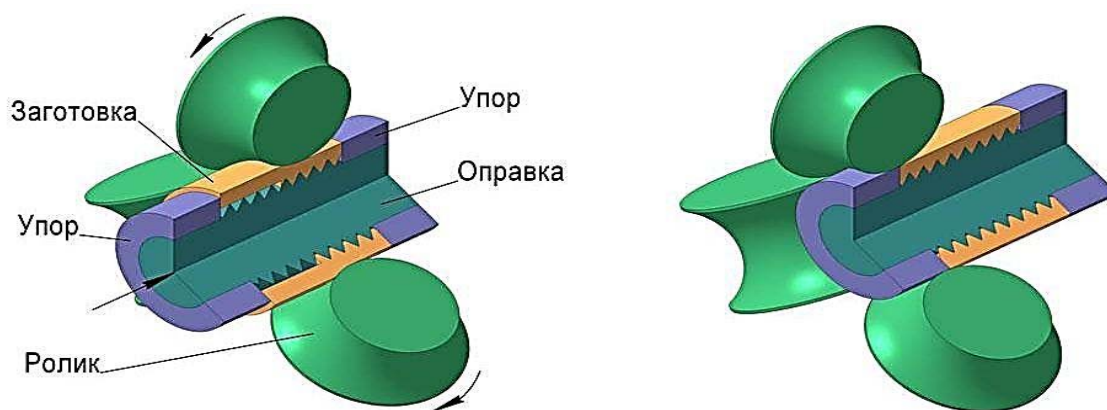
Способ выдавливания резьбы обкатыванием роликами, расположенными в плоскости перпендикулярной оси заготовки
